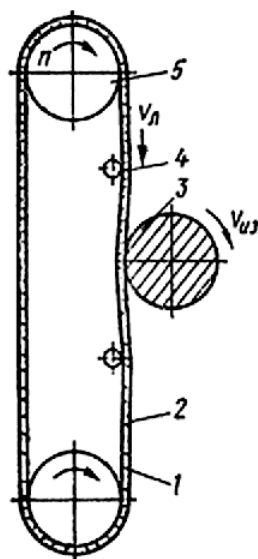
Схема устройства для ленточного шлифования деталей
